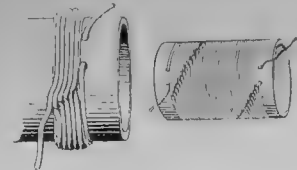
Способ намотки и общий вид готовой двуслойной катушки.
